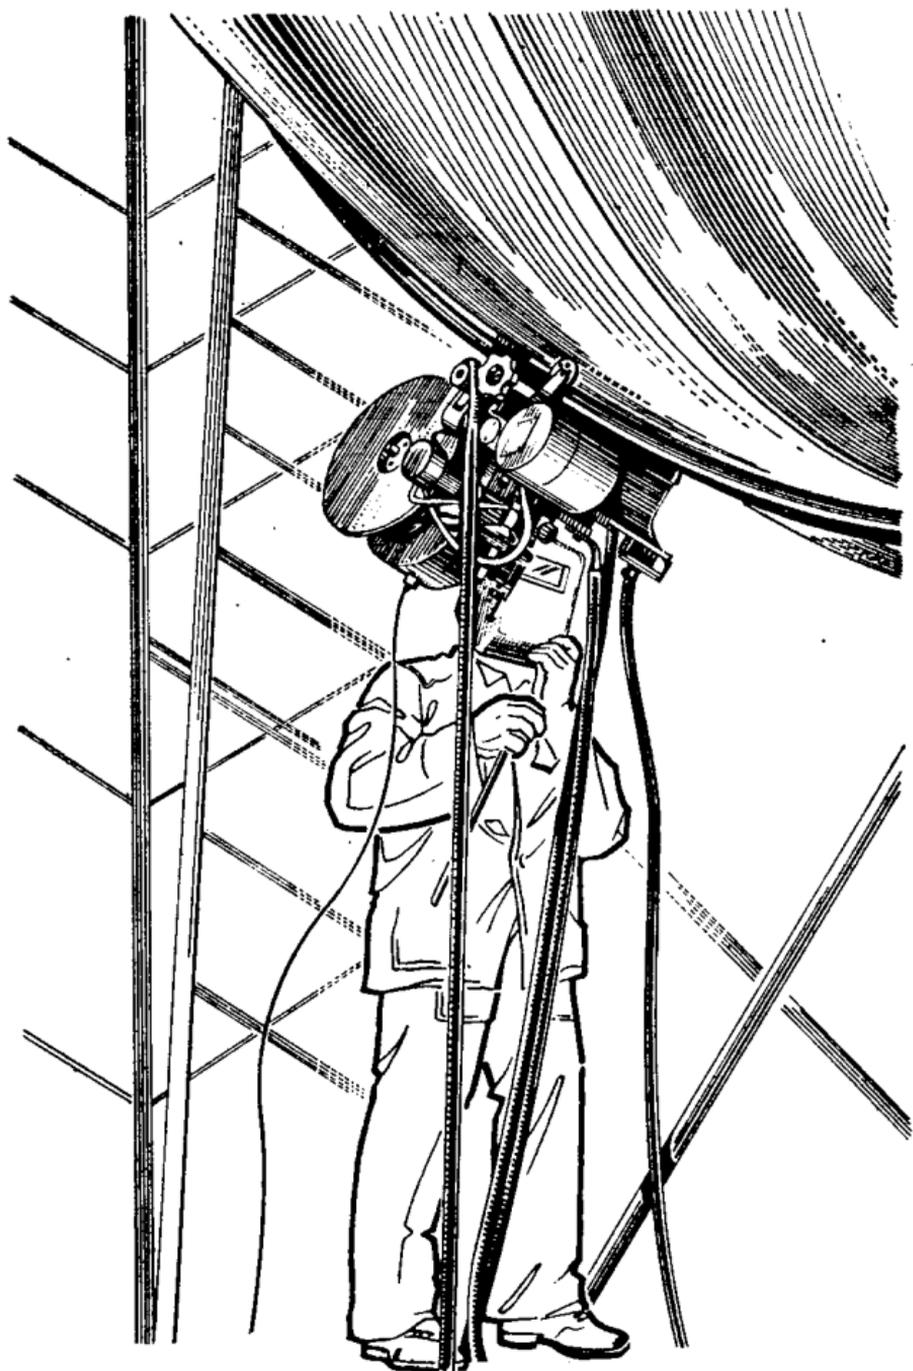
Сварка неповоротного стыка сферической оболочки аппаратом А-1381.
